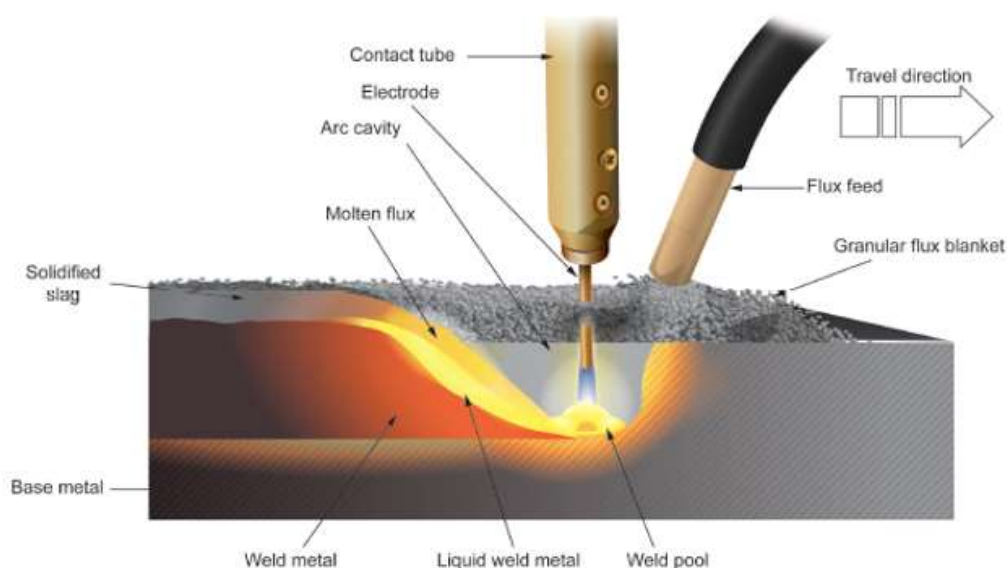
Схема автоматичного зварювання під флюсом
